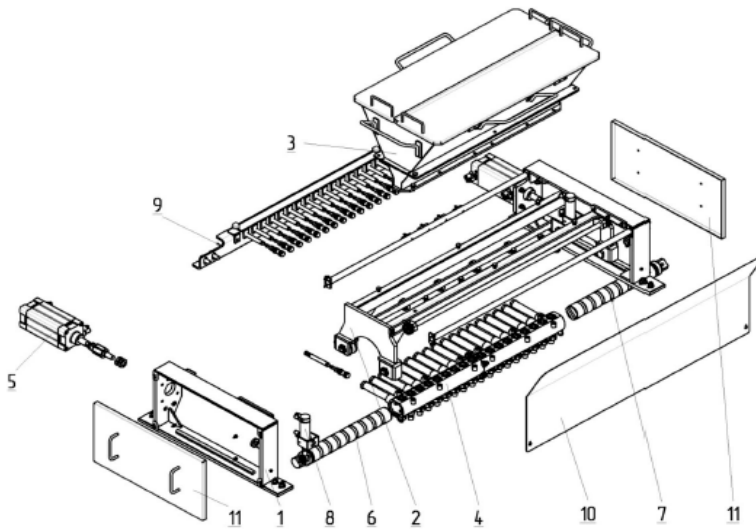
Конструкція дозатору тіста: 1 – опора дозатора, 2 – супорт, 3 – бункер, 4 – корпус дозатора, 5 – пневмоциліндр привідний, 6 – затвор лівий, 7 – затвор правий, 8 – пневмоциліндр затвору, 9 – плита з поршнями, 10 – захисний кожух, 11 – захисні кришки
